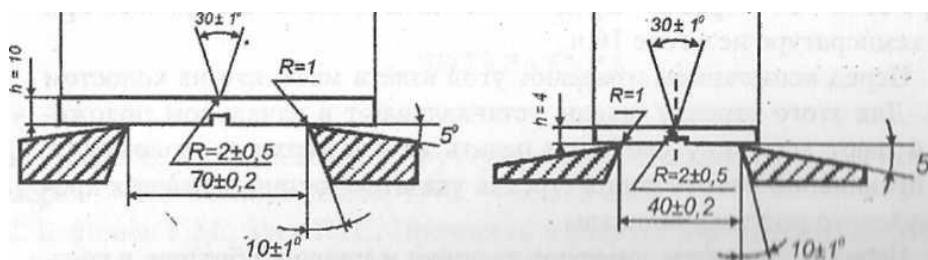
а - нож и опоры для стандартного бруска с надрезом; б - для стандартного бруска без надреза.
